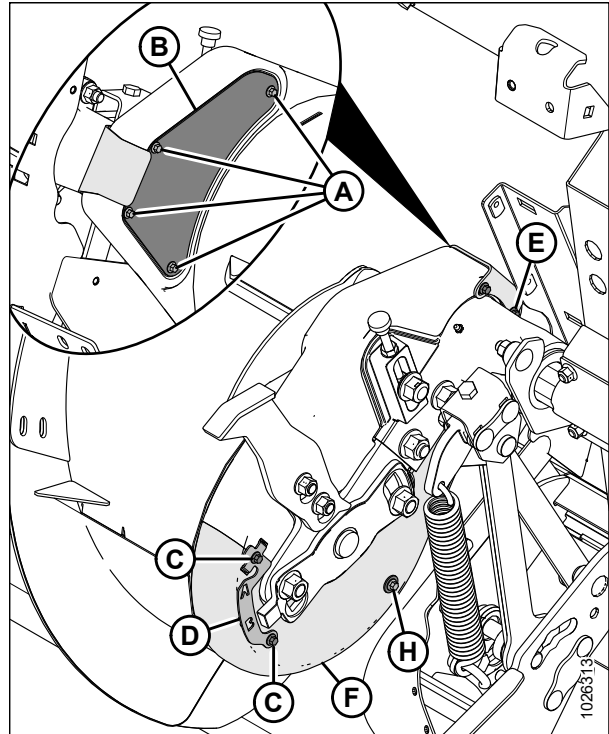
Einzugstrommelgetriebe – Rückansicht
